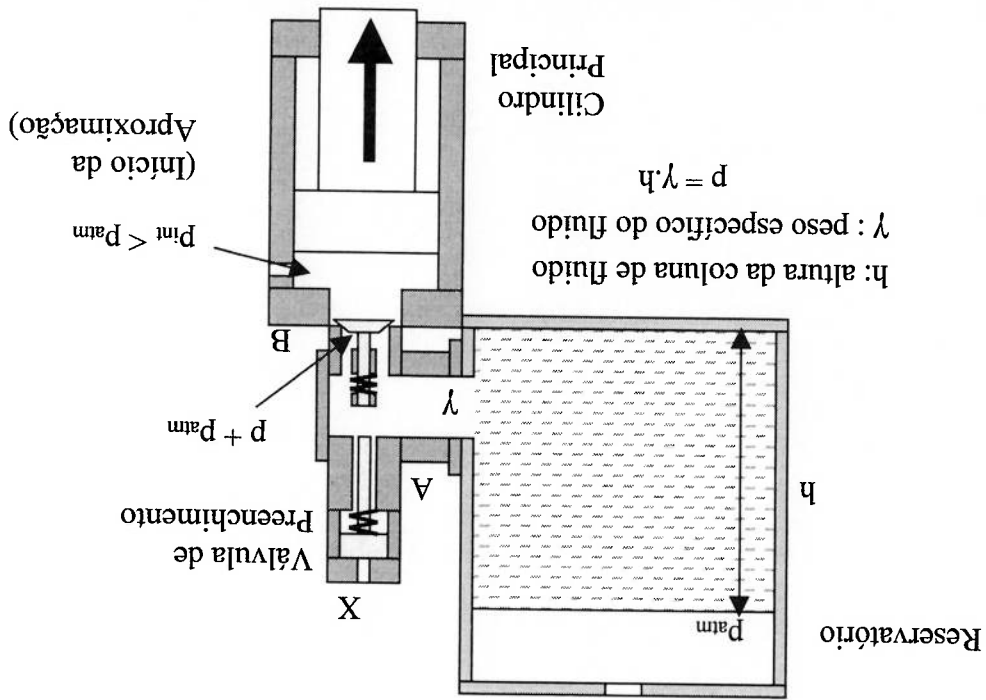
Instalação de Prensa com Válvula de Preenchimento
